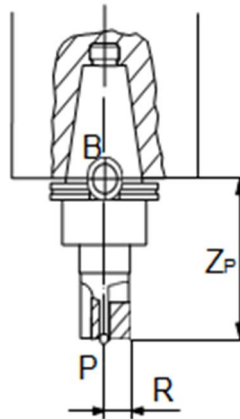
Розташування точки установки інструменту на фрезерному верстаті з ЧПК
